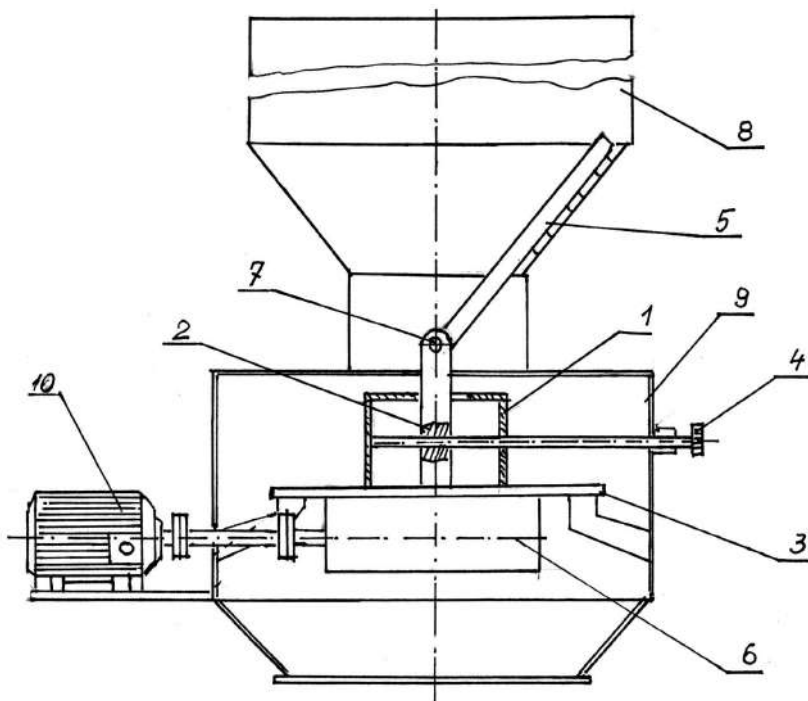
Разрабатываемый тарельчатый дозатор:
